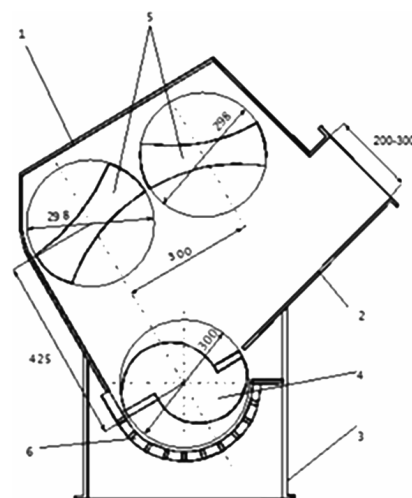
Схематическая конструкция дробилки ДАУ-250: 1 – корпус дробилки; 2 – загрузочный патрубкок; 3 – разгрузочный отсек; 4 – первичный ротор; 5 – вторичные ротора; 6 – разгрузочное решето
